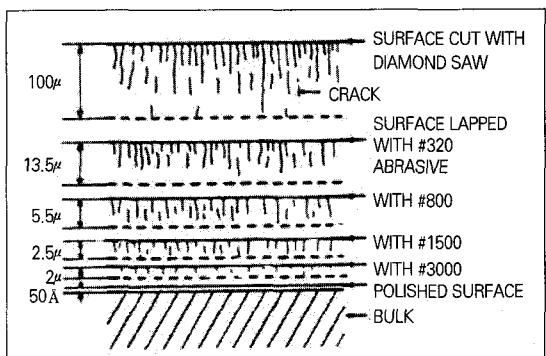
Optical glass의 각종 가공시 발생한 crack층의 깊이
